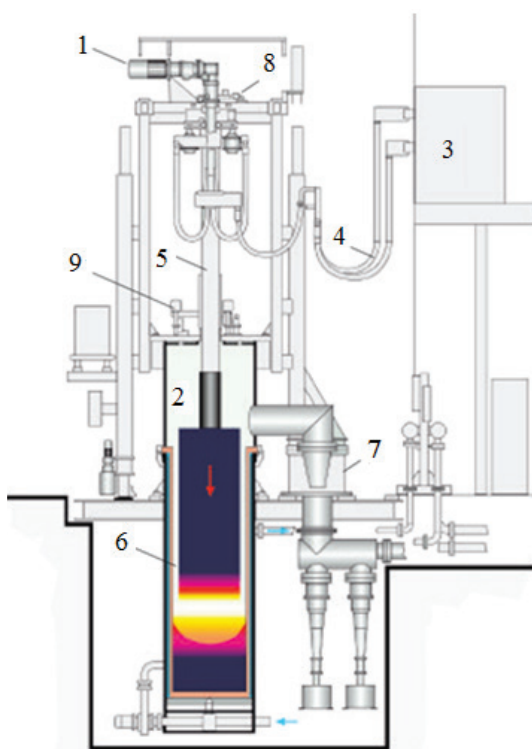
Схема установки вакуумно-дугового переплава:
